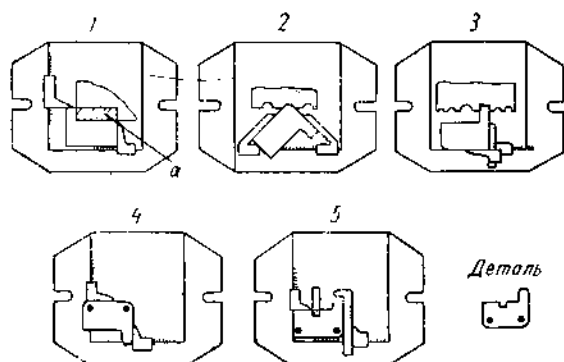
Пример последовательной штамповки по элементам на универсальных штампах:
